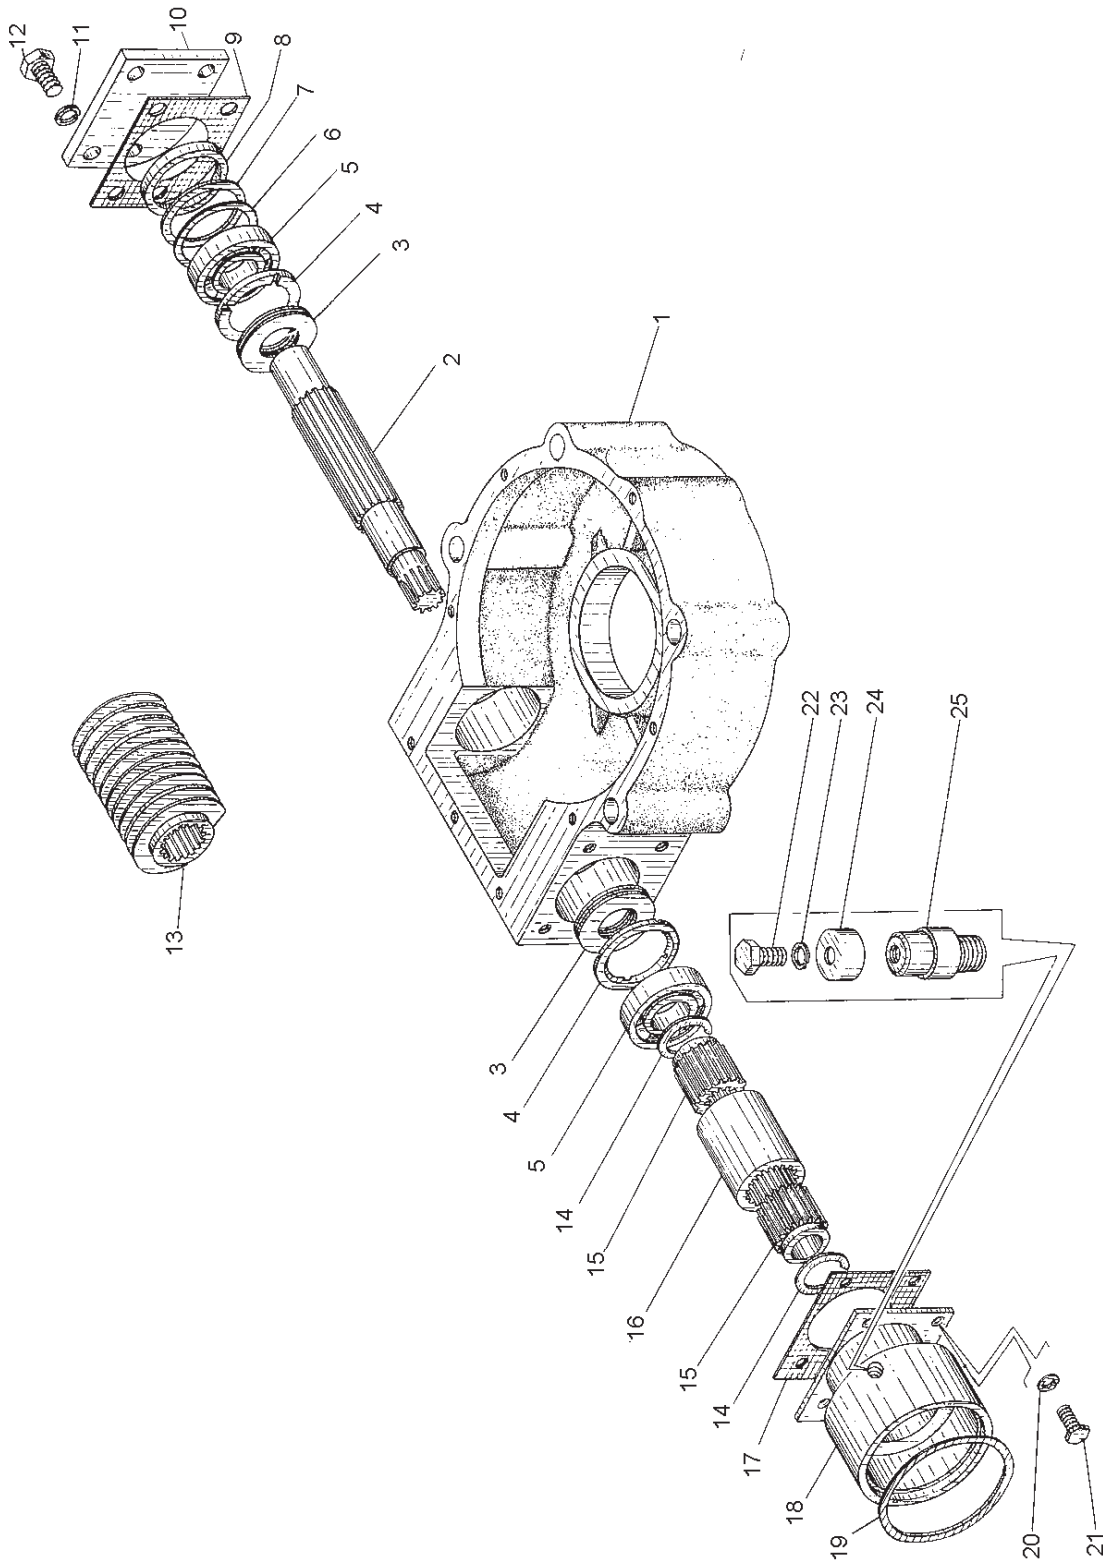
Редуктор поворота отвала (ДЗ-98.29.00.000)
